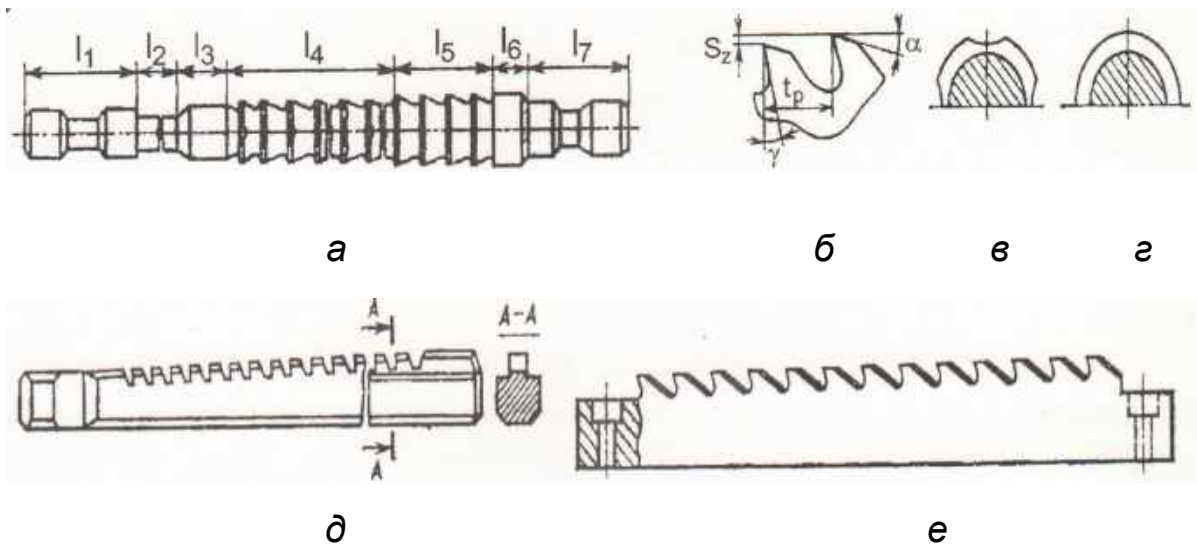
Інструменти для оброблення поверхонь заготовок на протяжних верстатах: а – круга протяжка; б – поздовжній переріз двох зубів; в – поперечний переріз робочої частини протяжки; г – поперечний переріз калібрувальної ділянки; д – протяжка для формотворення паза в отворі; е – протяжка для виготовлення зовнішньої площини
